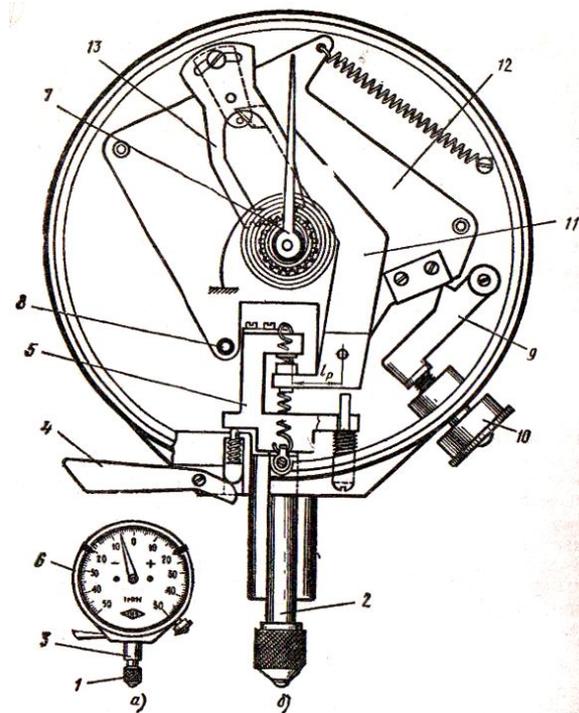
Однооборотная измерительная головка ИГ: а – общий вид; б – конструктивная схема
